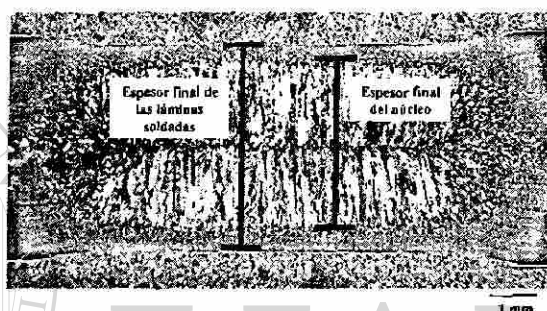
Medición de la penetración real en la soldadura.
